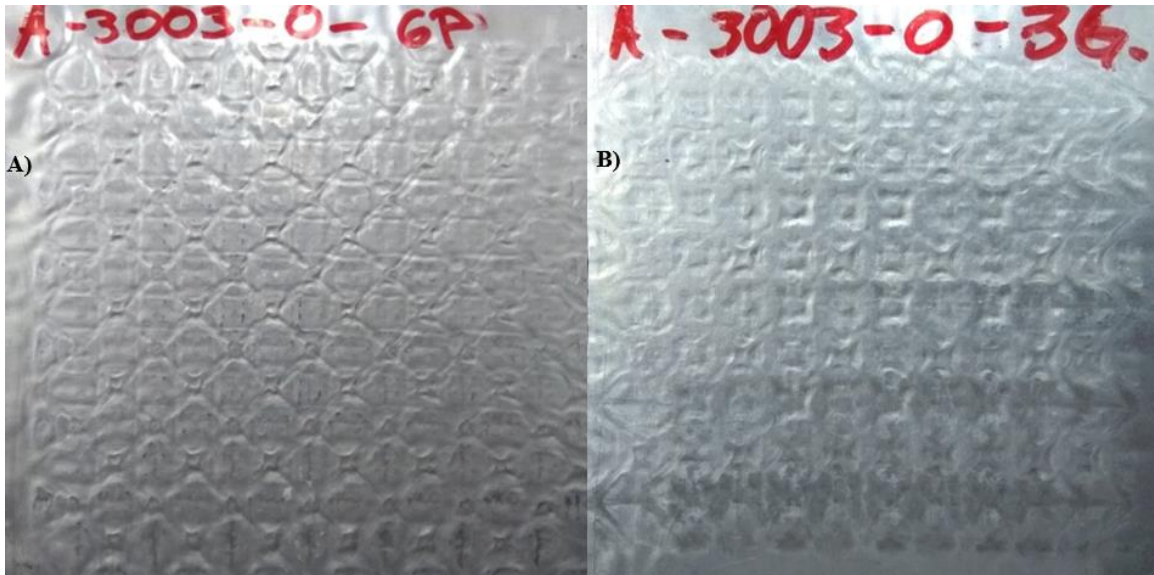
Láminas muestra sin fracturas producida por el molde de acero. A) Serie “P”, B) Serie “G”.
